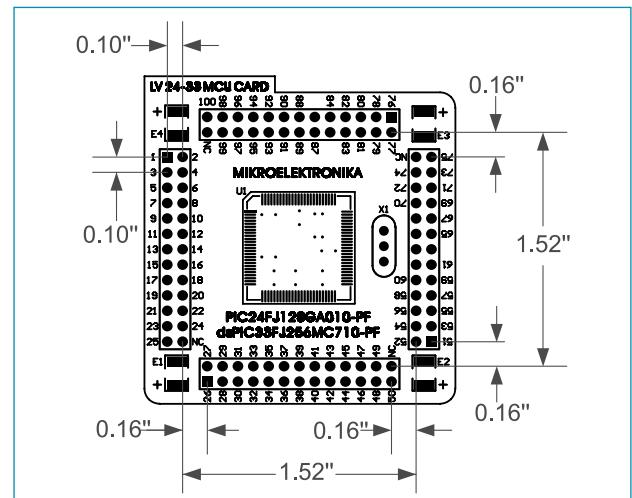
Dimensiones de la tarjeta MCU para las MCU Card 1 a MCU Card 8
